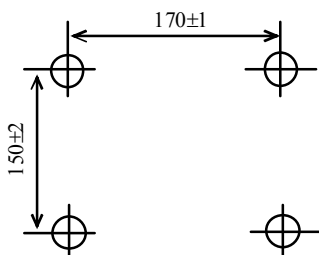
Разметка отверстий для крепления тепловычислителя.
